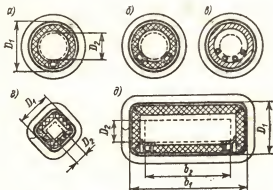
Варианты конструкций и расположения направляющих: а — индуктор для нагрева цилиндрических заготовок с диаметрами до 80 мм; б — то же, но с диаметрами больше 80 мм; в — индуктор для нагрева цилиндрических заготовок с трубчатыми цилиндрическими направляющими; г — индуктор для нагрева заготовок с квадратным поперечным сечением; д — индуктор для нагрева заготовок с прямоугольным поперечным сечением. (Буквенные обозначения приведены в расчетах)
